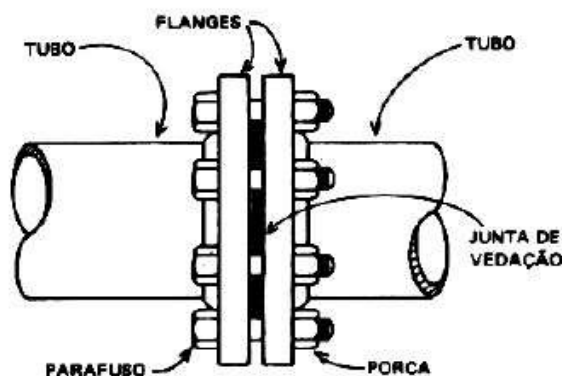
Desenho Representativo de uma Conexão Flangeada. (SENAI, 1997)
